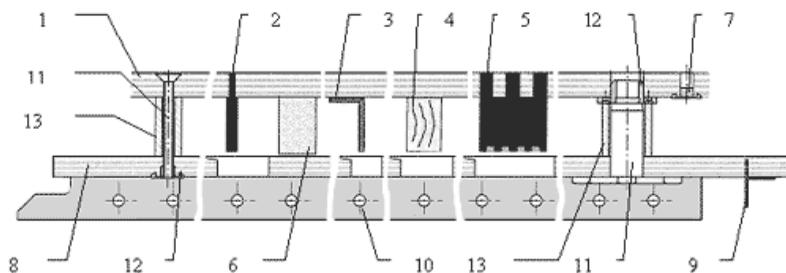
Конструкция оснастки для удаления отходов: 1 — фанерное основание; 2–5 — пуансоны; 6 — прижимное устройство; 7 — деталь для крепежа к штанцевальной машине; 8 — слой фанеры; 9 — линейка для сепарирования отходов; 10 — балки для крепления в штанцевальной машине; 11–12 — винты, гайки; 13 — промежуточные втулки
